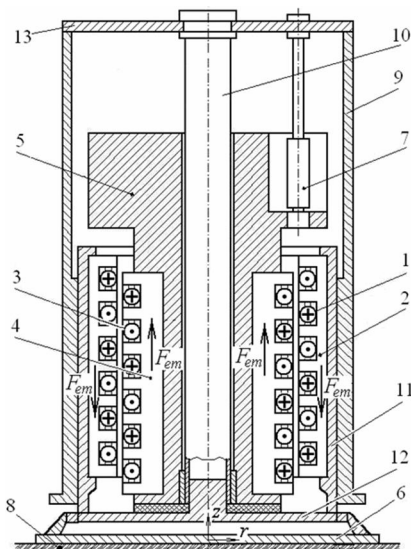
Устройство ЛИЭД: 1, 3 – кольцевые обмотки якоря и реактора; 2, 4 – коаксиальные шихтованные сердечники якоря и реактора; 5 – внутренний каркас реактора, совмещенный с инерционной массой; 6 – опорный конус; 7 – амортизатор; 8 – грунт; 9 – корпус наружный; 10 – колона направляющая; 11 – корпус якоря; 12 – плита с направляющим стаканом; 13 – верхний щит
